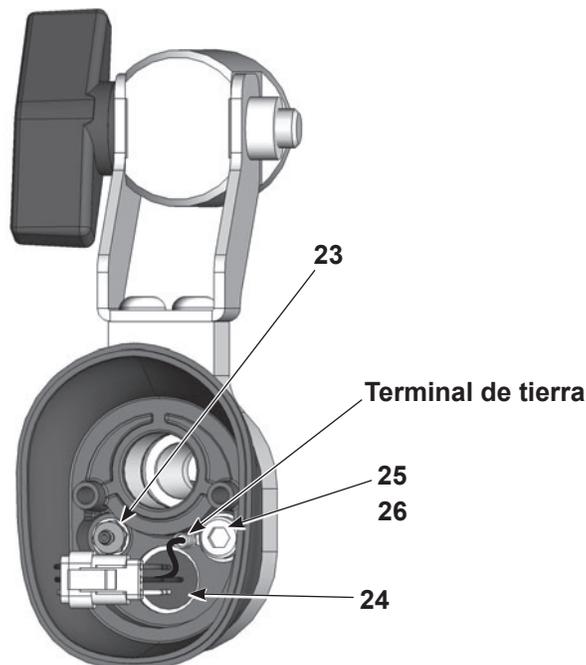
Desmontaje de la pistola - Sustitución del receptáculo para cable y del racor dentado
